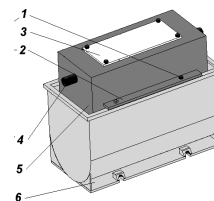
Конструкция рабочей камеры для ВиАУЗО деталей в свободном состоянии с расположением ультразвукового преобразователя над рабочей камерой: 1 – резьбовые соединения; 2 – крепление; 3 – смотровой люк; 4 – штуцер для подачи охлаждающей жидкости; 5 – ультразвуковой преобразователь; 6 – рабочая камера
